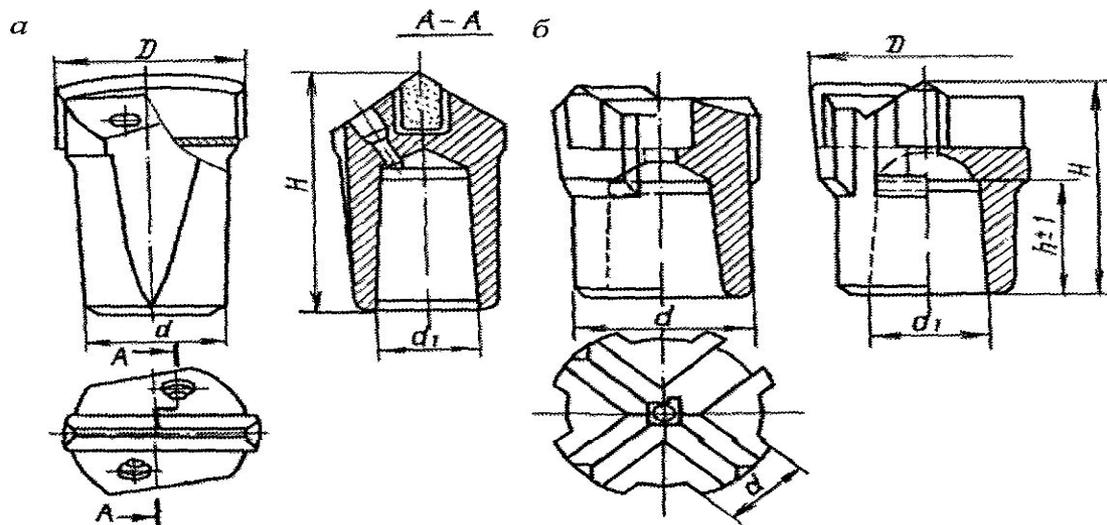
Буровые коронки с твердосплавными вставками для пневмоударного бурения:
